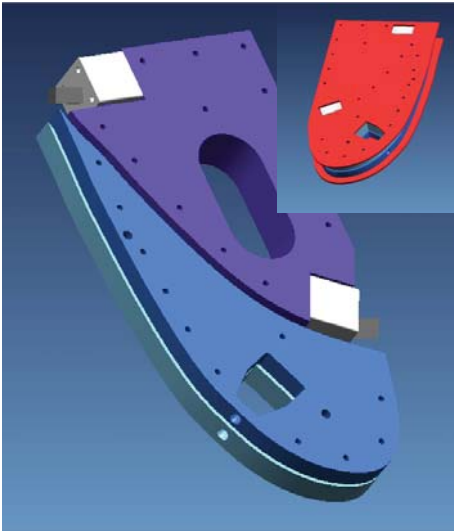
CAD-Zeichnung des Rippenwerkzeugs
